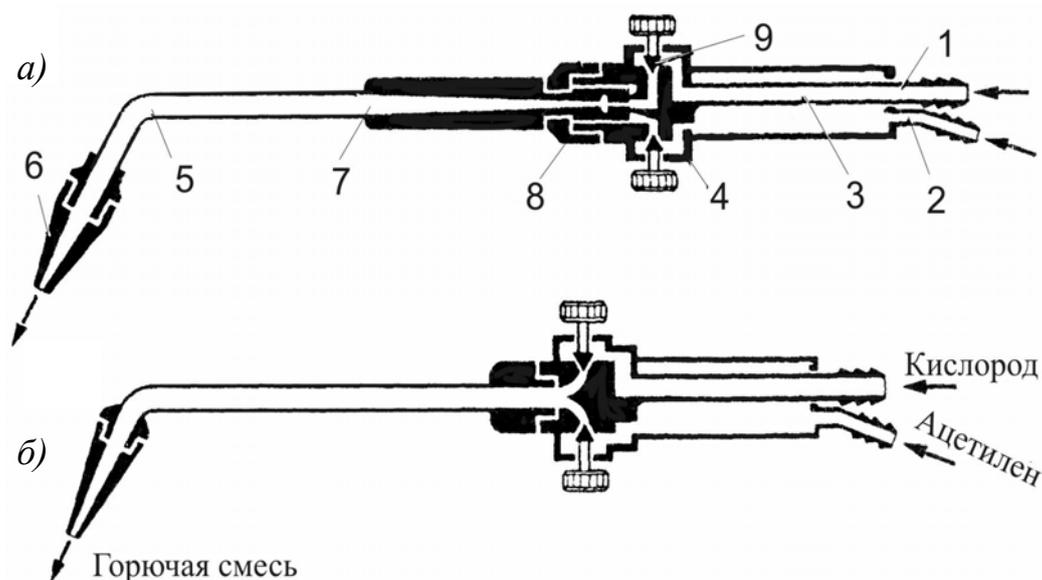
Схемы сварочных горелок: а – инжекторная; б – безынжекторная; 1 – ниппель подачи кислорода; 2 – ниппель подачи горючего; 3 – трубка; 4 – корпус горелки; 5 – наконечник; 6 – мундштук; 7 – смешивательная камера; 8 – инжектор; 9 – кислородный вентиль
